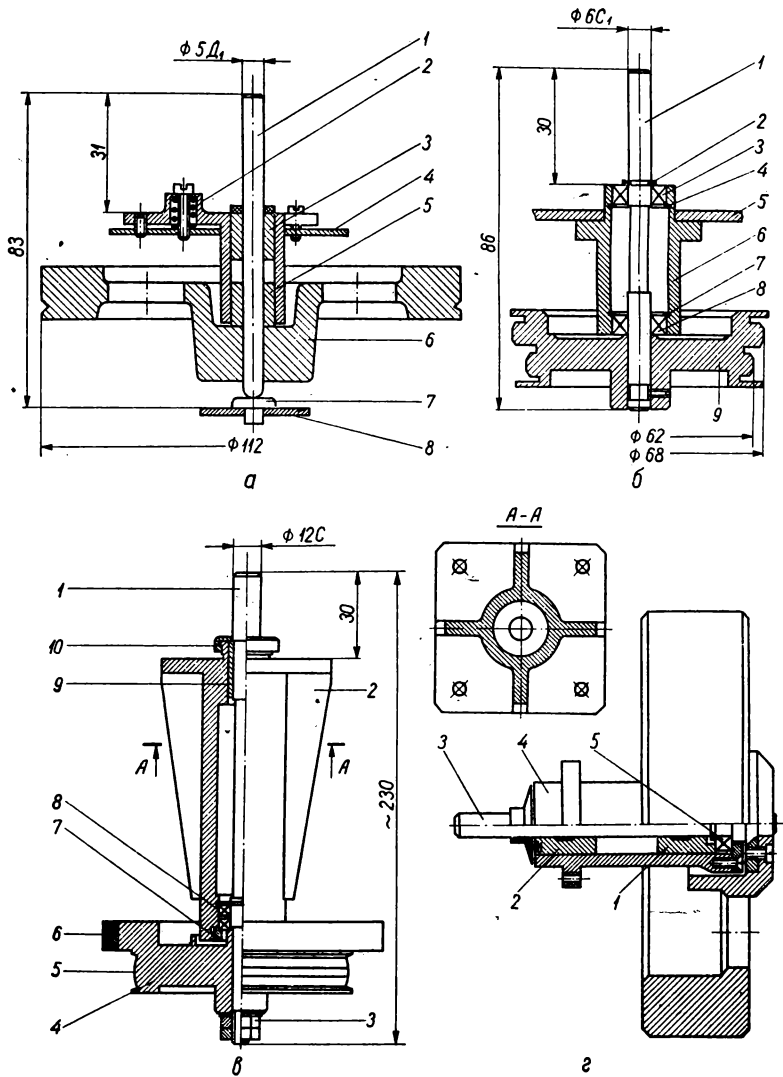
Типовые конструкции узлов ведущего вала исполнения II.
